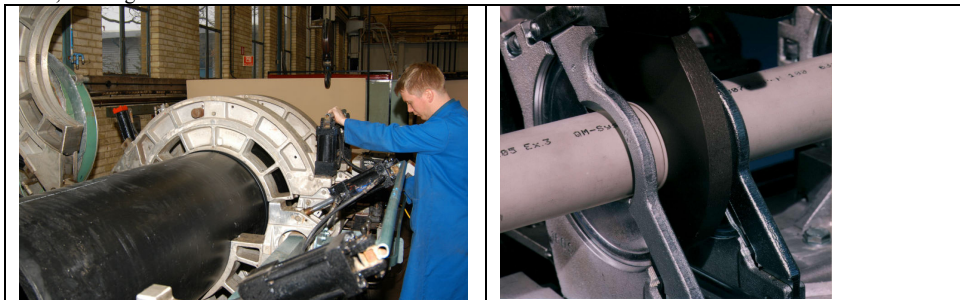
Soldadura de tubos a tope (TWI)
